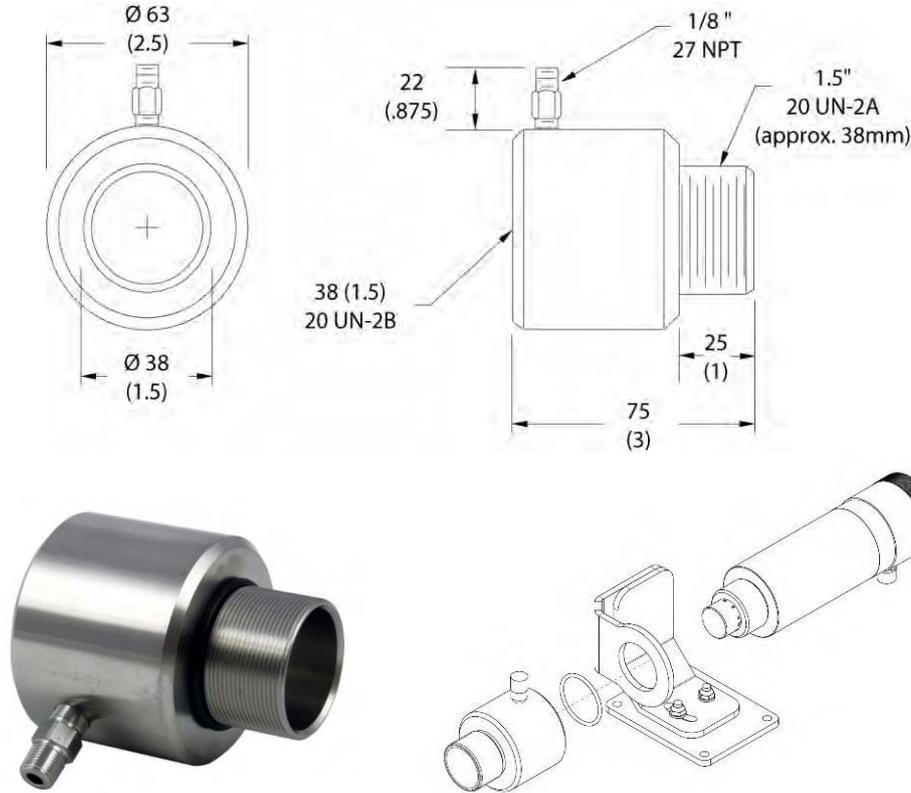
Vue et dimensions du collier de purge à air (E-AP)
